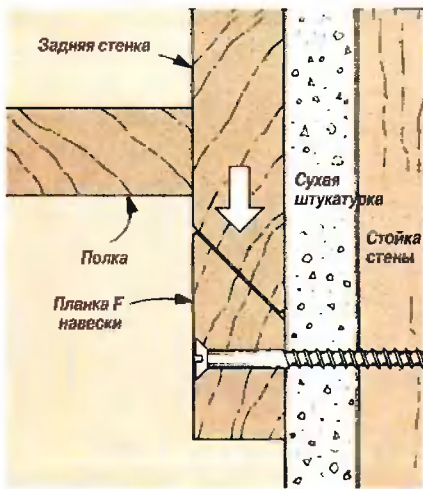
Крепление вешалки к стене. Вешалку надевают нижней скошенной кромкой задней стенки на ответную планку F с фаской, прикрепленную к стойкам стены.
